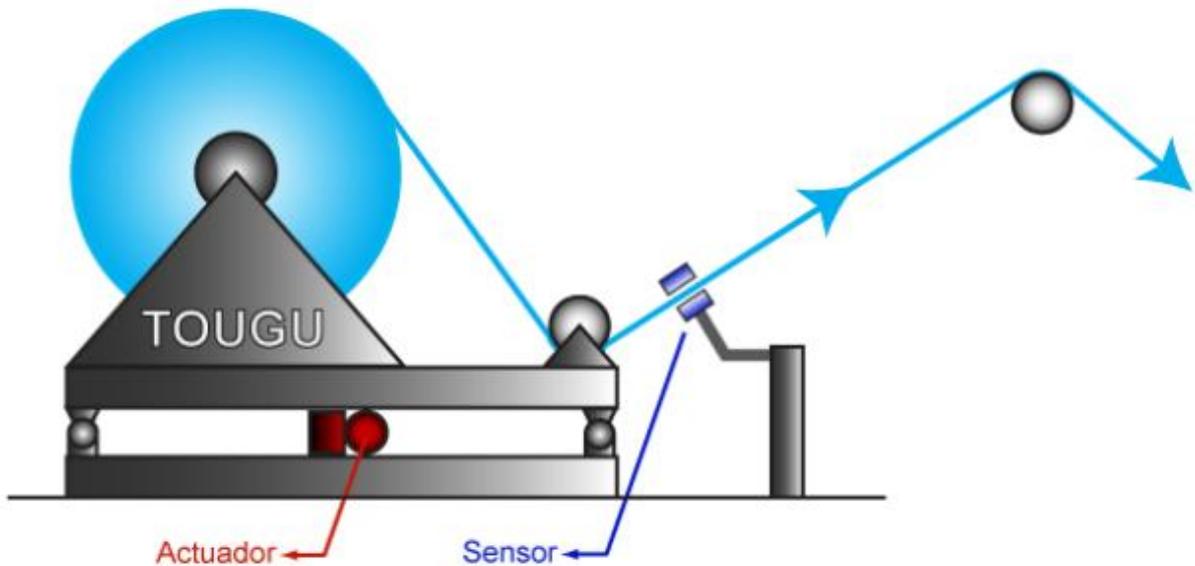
Guiador de banda por borde o centro para desenrollado
